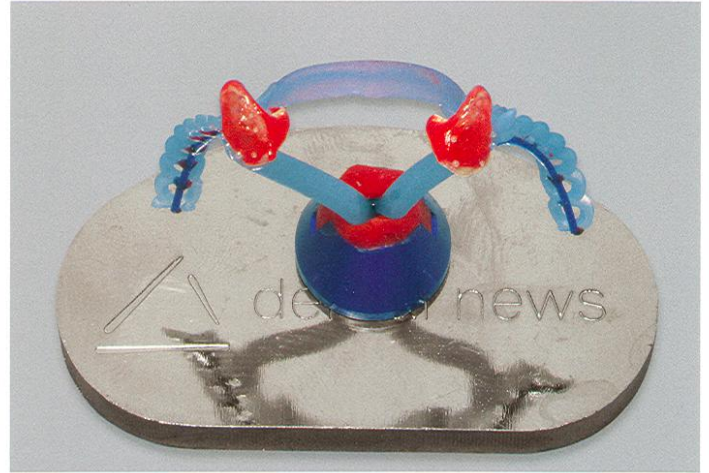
Gussobjekt auf dem magnetischen Gusstrichter und der Sockelplatte. Der Gusstrichter mit dem Objekt kann hier auch wieder in die richtige Position gebracht werden.
